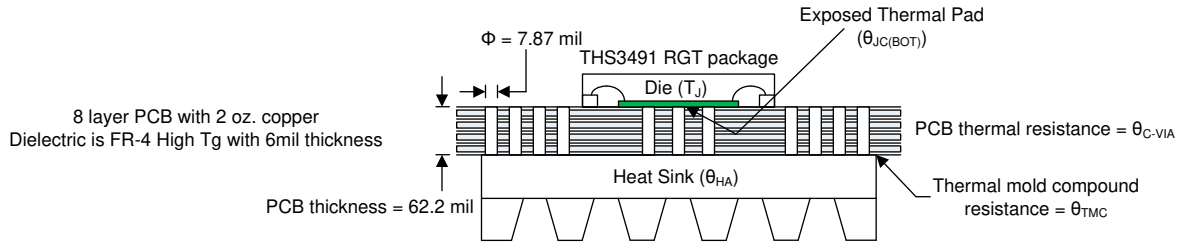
不同热阻的 TIDA-060033 PCB 横截面
